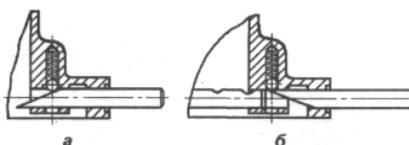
Приспособление для сборки штоков и фиксаторов механизма переключения коробки передач: А) – сборка фиксатора;Б) – установка штока.
